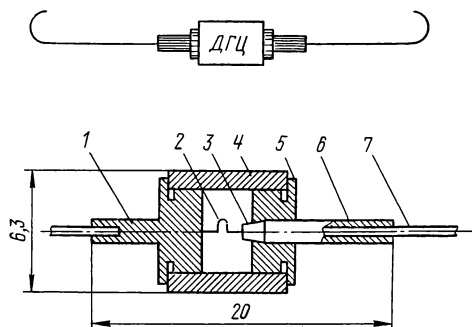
Внешний вид и схема устройства германиевого выпрямителя:
